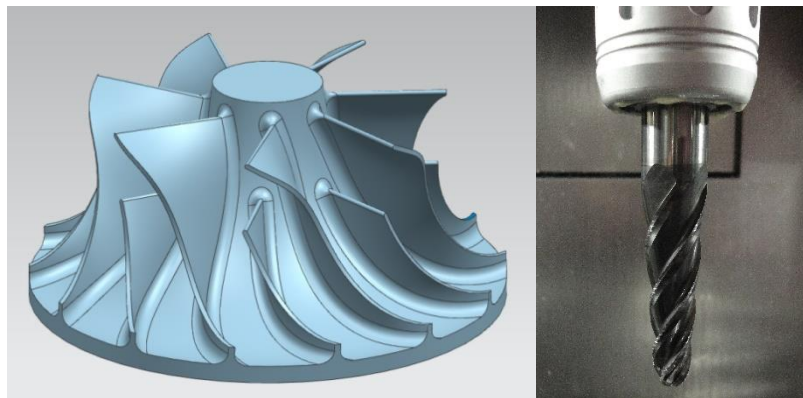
4 Geometría de impeller a mecanizar y fresa cónica de desbaste utilizada
